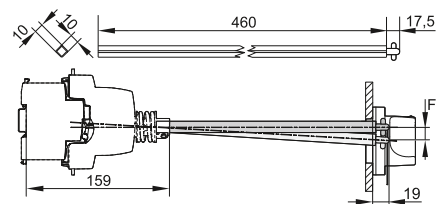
Габаритные размеры штока и расстояние смещения штока F по вертикали / Figure 3 – Overall dimensions of the rod and displacement range F vertically
